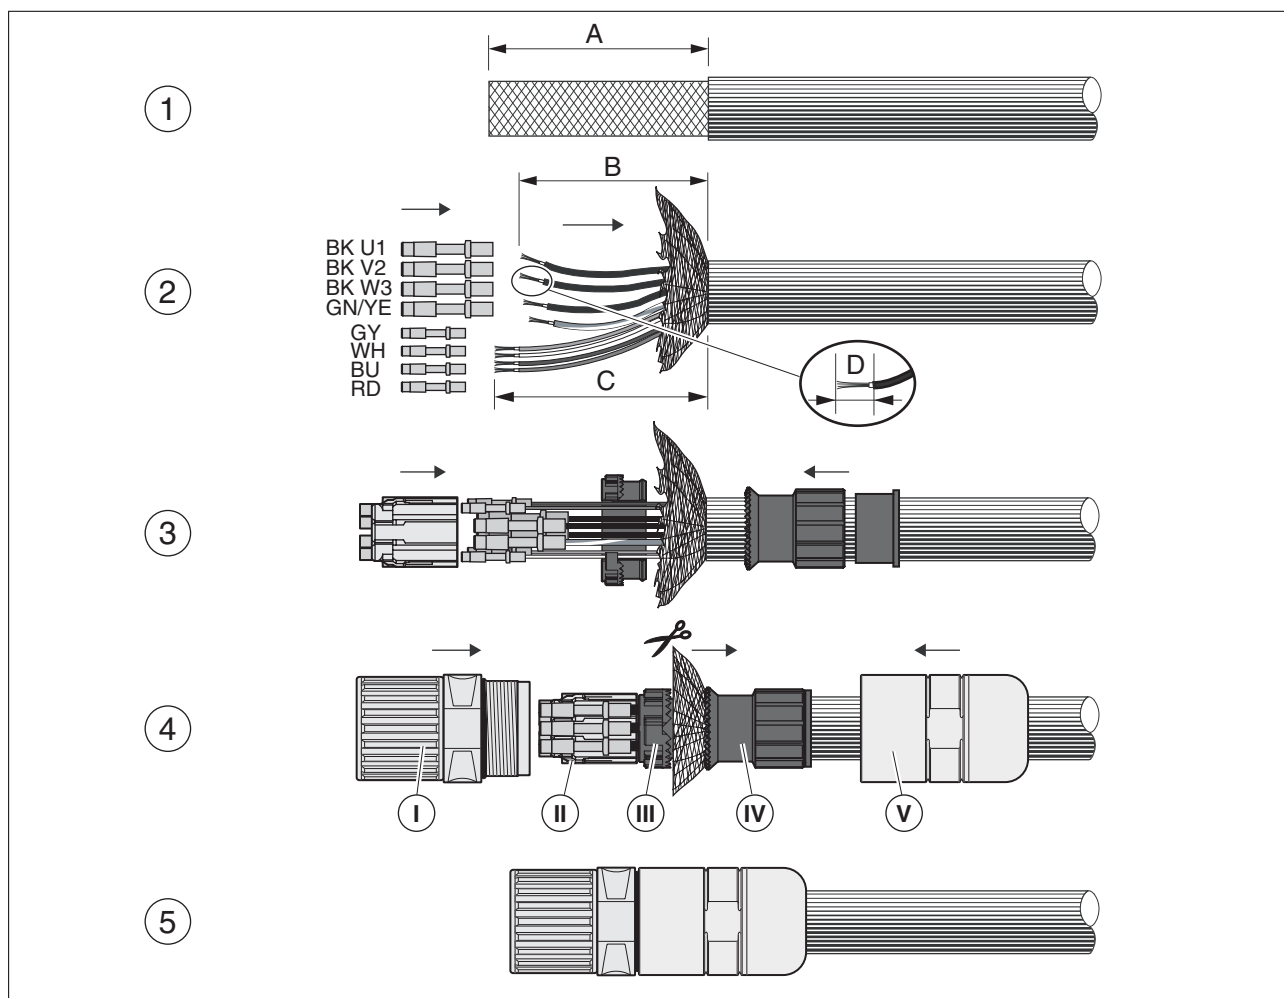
Assemblare il cavo motore con connettore motore M23
